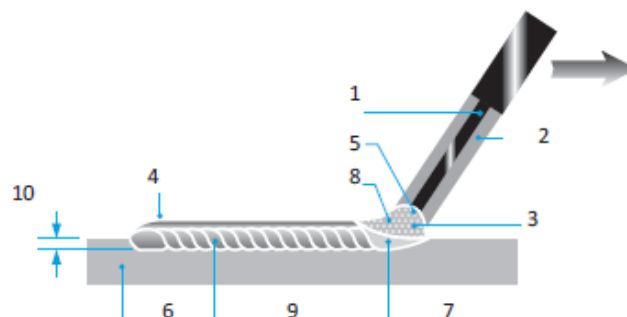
Principio de funcionamiento de la soldadura eléctrica
